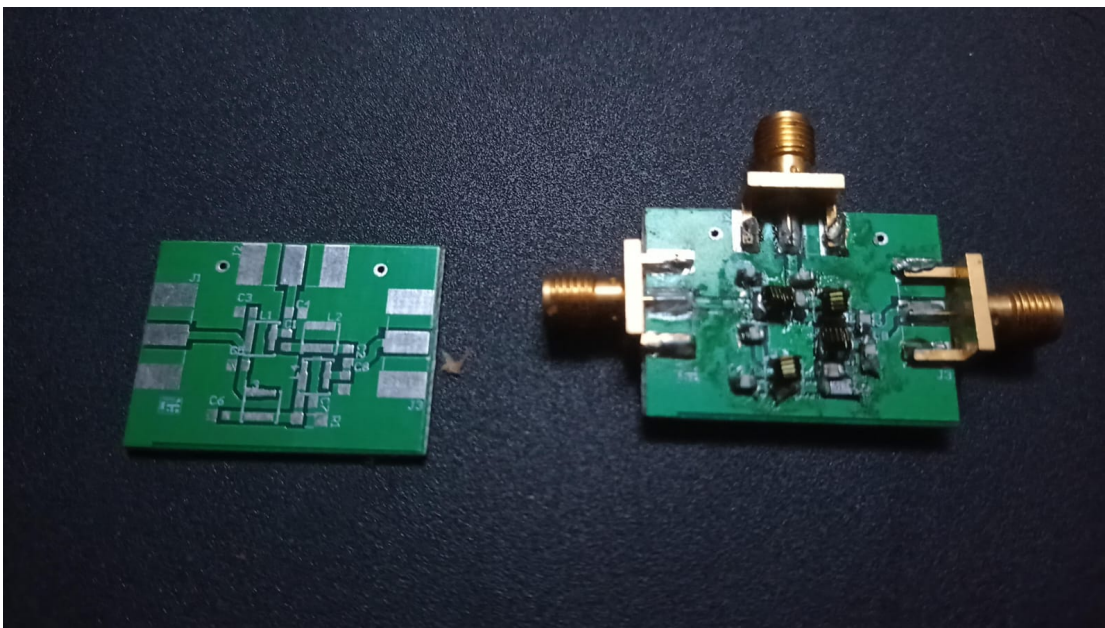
Placa de Circuito Impresso do circulator: sem; e com os componentes eletrônicos soldados na placa.
